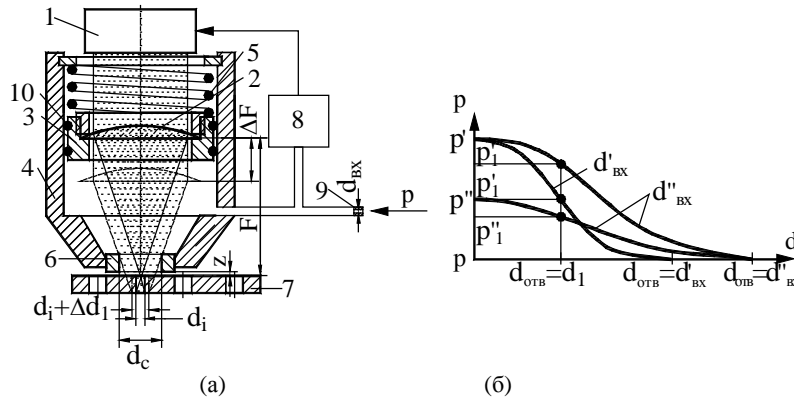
Схема ЛТУ с устройством для адаптивной организации операции для обработки отверстий (а), пневматическая характеристика системы (б). (1 – лазер; 2 – линза; 3 – оправка-поршень; 4 – корпус-пневмоцилиндр; 5 – пружина; 6 – сопло; 7 – заготовка; 8 – датчик давления; 9 – входная диафрагма; 10 – уплотнение).
